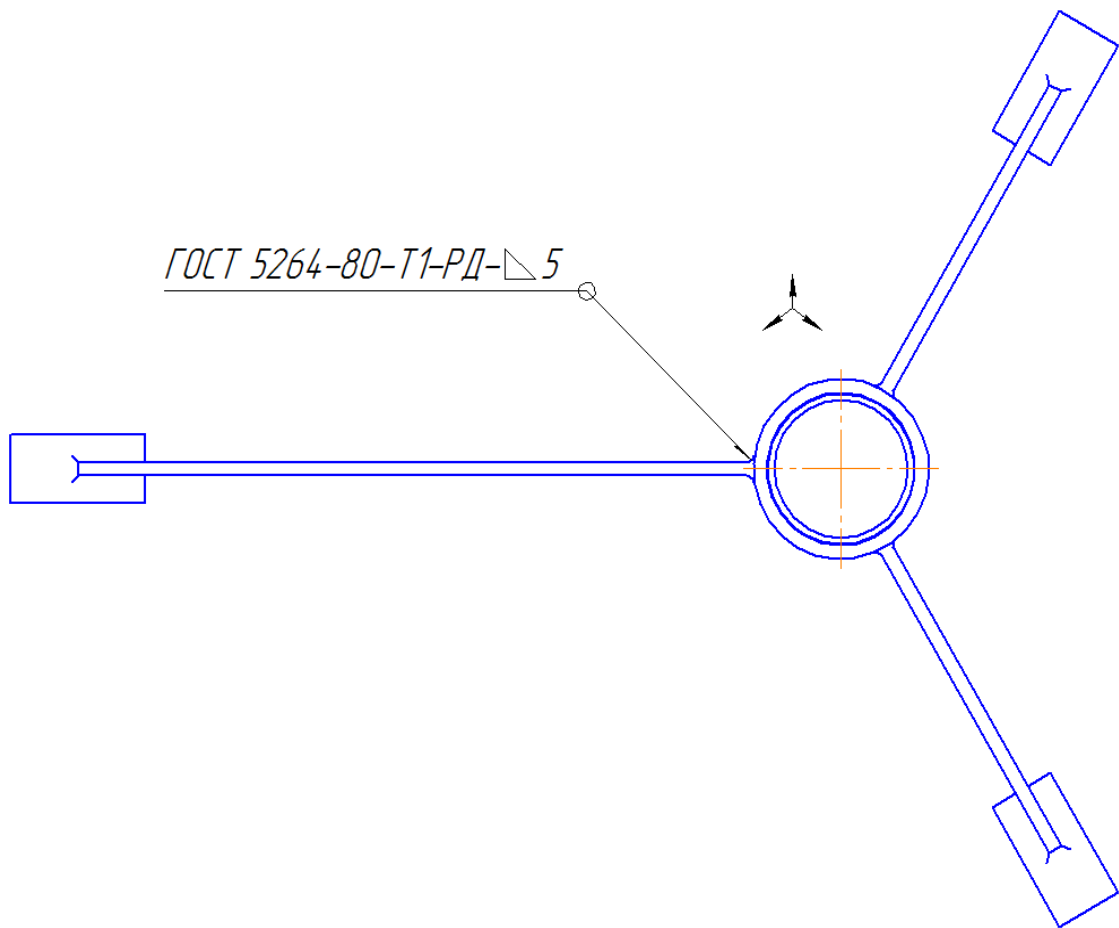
Сварка ножек стойки с наружной трубой
